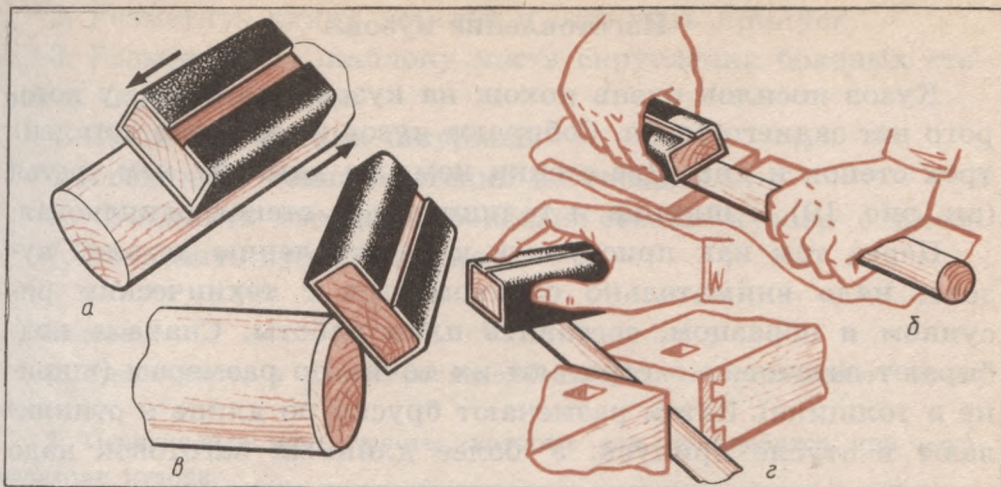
Зачистка круглой ручки шкуркой на подушке: *а* — направление движения шкурки; *б* — захват заготовки; *в* — скругление углов; *г* — зачистка зажатой ручки.
